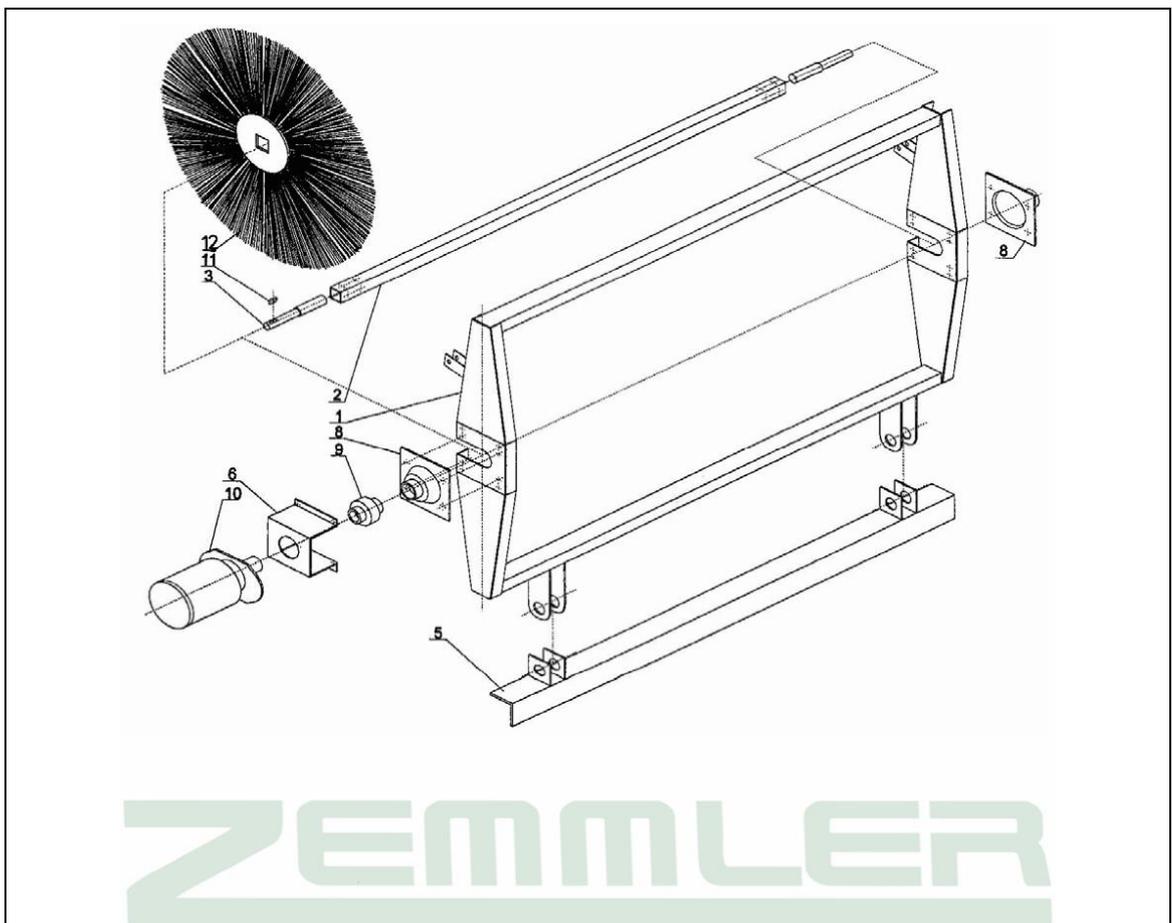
Installazione e fissaggio dell'elemento delle spazzole
